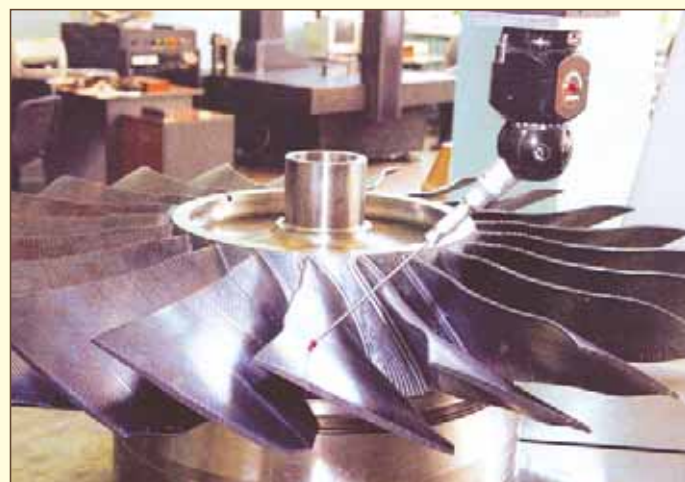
Участок координатно-измерительных установок с ЧПУ. Контроль профиля пера лопаток моноколеса компрессора
